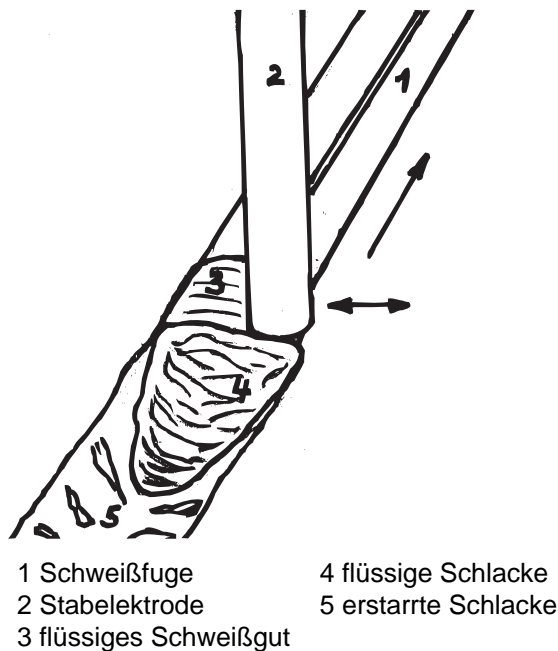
Stellung der Elektrode in der Schweißfuge
